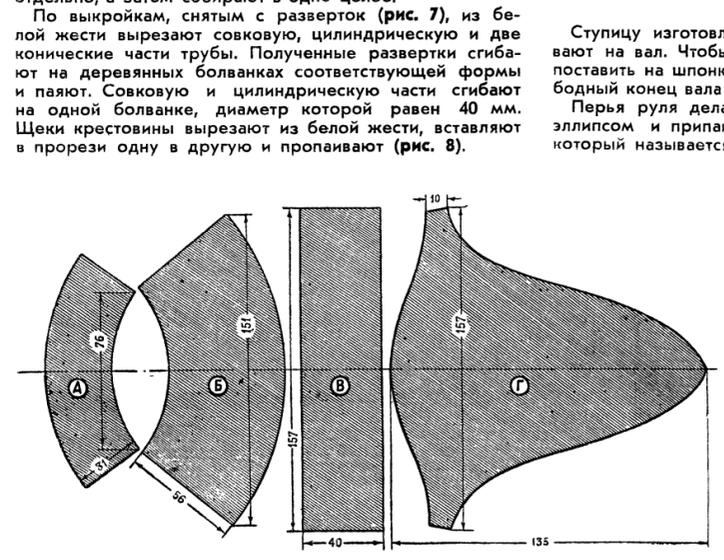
Развертка частей водометной трубы: А и Б — конические; В — цилиндрическая; Г — совковая
